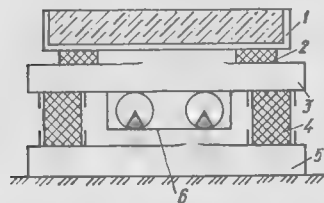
Принципиальная схема площадки СМЖ-538 конструкции ВНИИстрой-дормаша:
